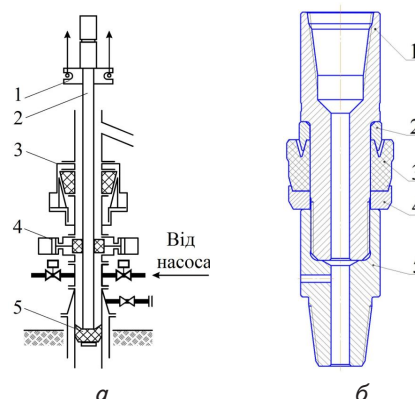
Пакер устьовий типу УВЧ: а – схема випробування плашкового превентора з використанням пакера (1 – елеватор, 2 – труба, 3 – універсальний превентор, 4 – плашковий превентор, 5 – пакер); б – конструктивне оформлення пакера (1 – корпус, 2 – втулка опорна, 3 – самоущільнювальна манжета, 4 – упор, 5 – перевідник)
